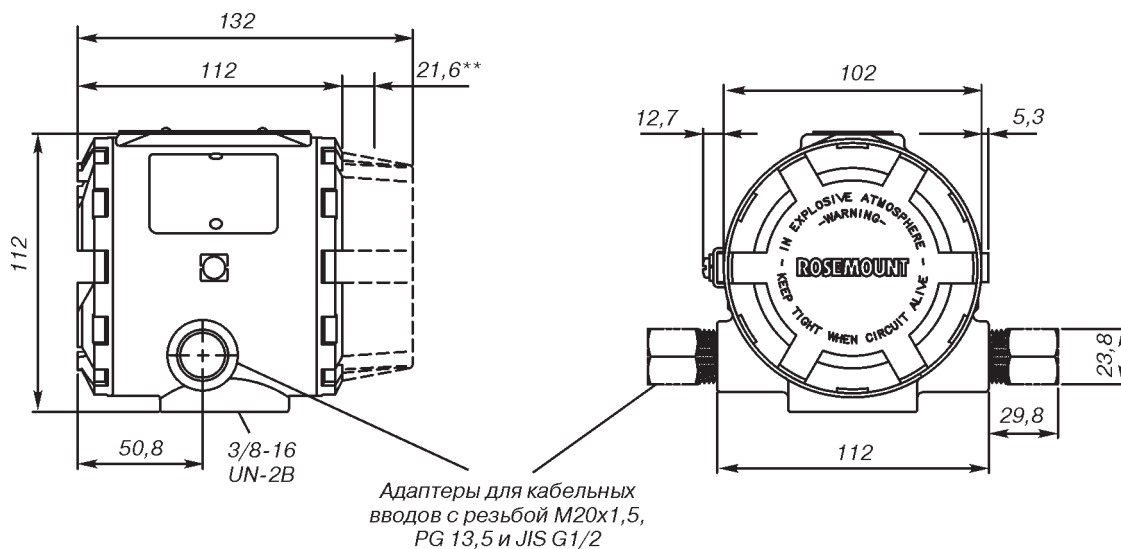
Габаритный чертеж преобразователя. Кабельный ввод M20x1,5; PG13,5 и JIS G1/2*.
